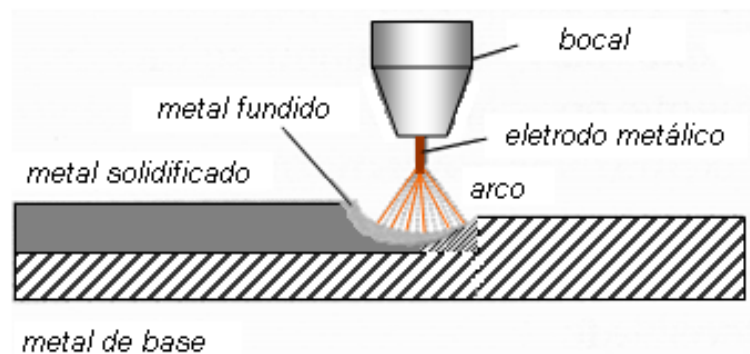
Esquema da soldagem GMAW (POEPCKE,1997)
